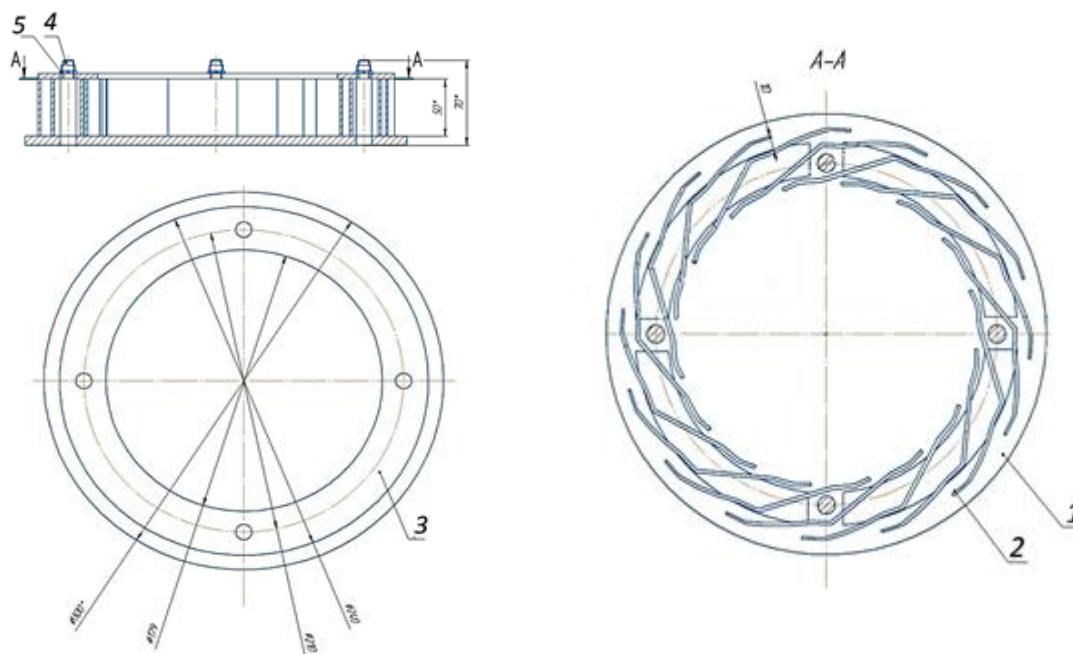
Завихритель с кольцевыми каналами: 1 – основание; 2 – профилированные пластины; 3 – крышка; 4 – шпилька; 5 – гайка
